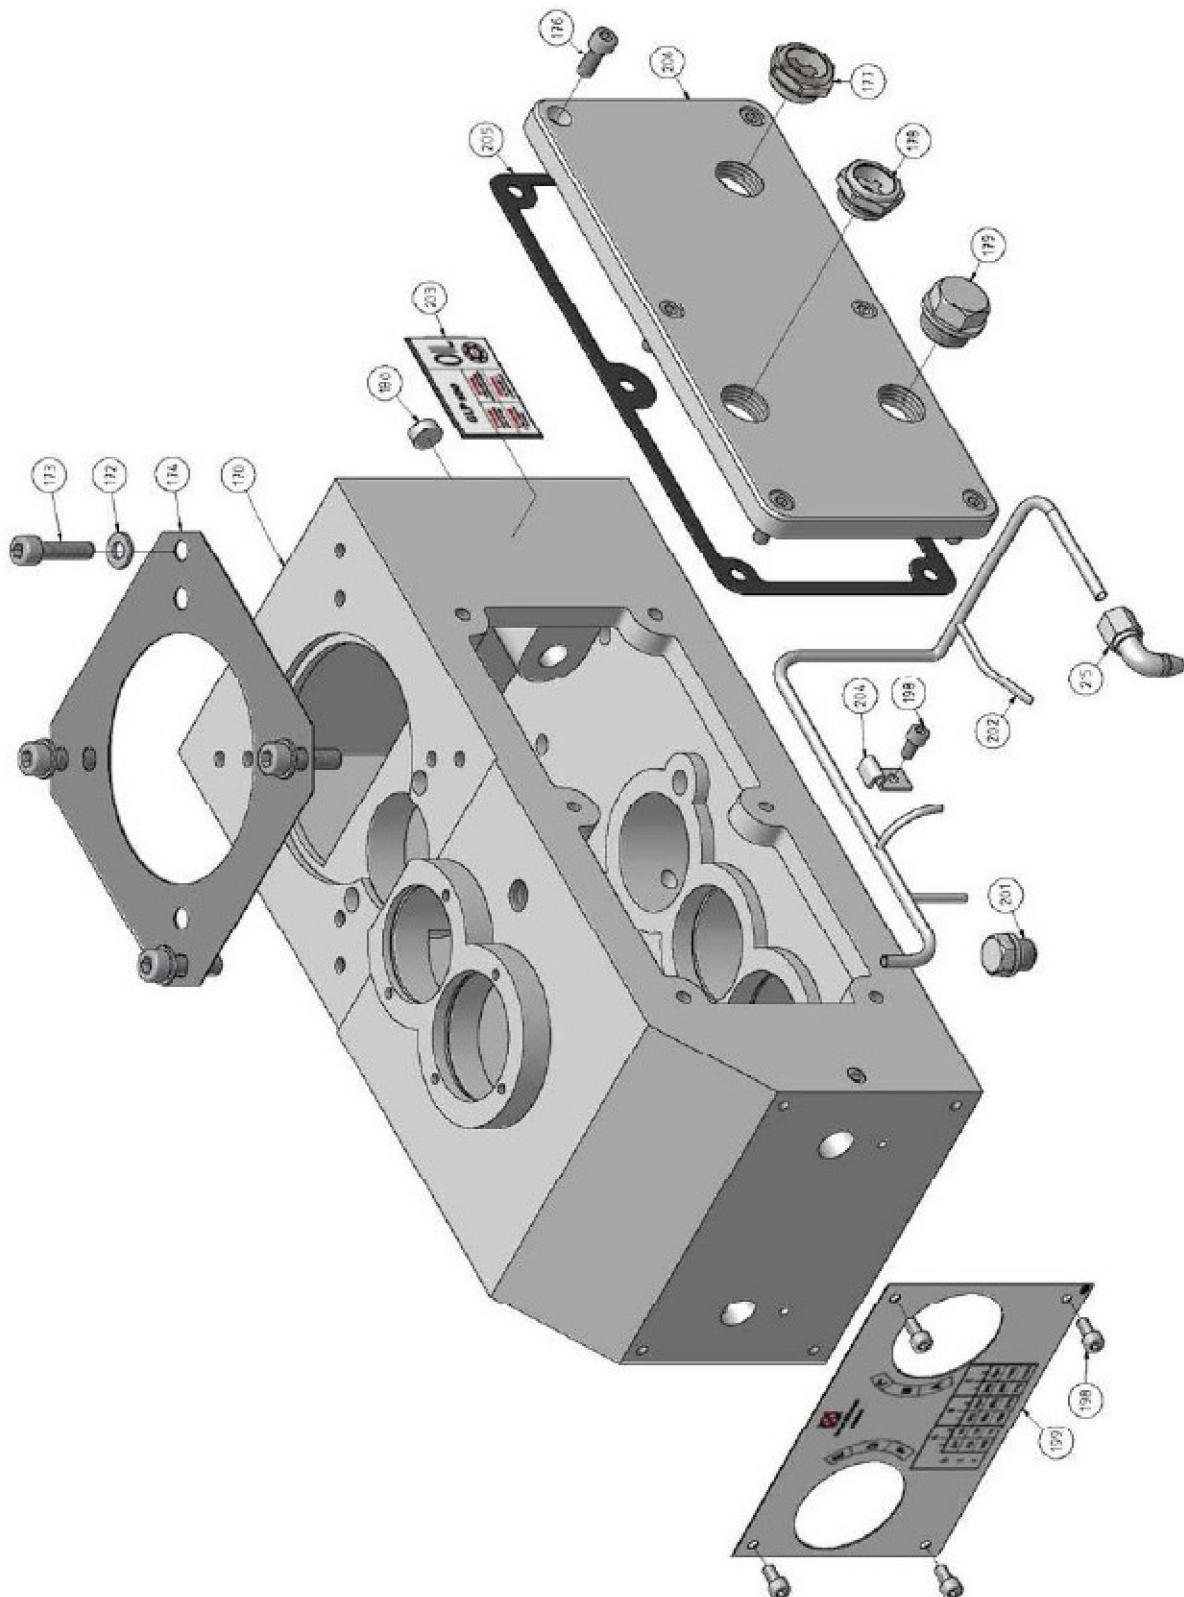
husillo principal caja de engranajes 4 de 4 - Gear box main spindle 4 of 4
